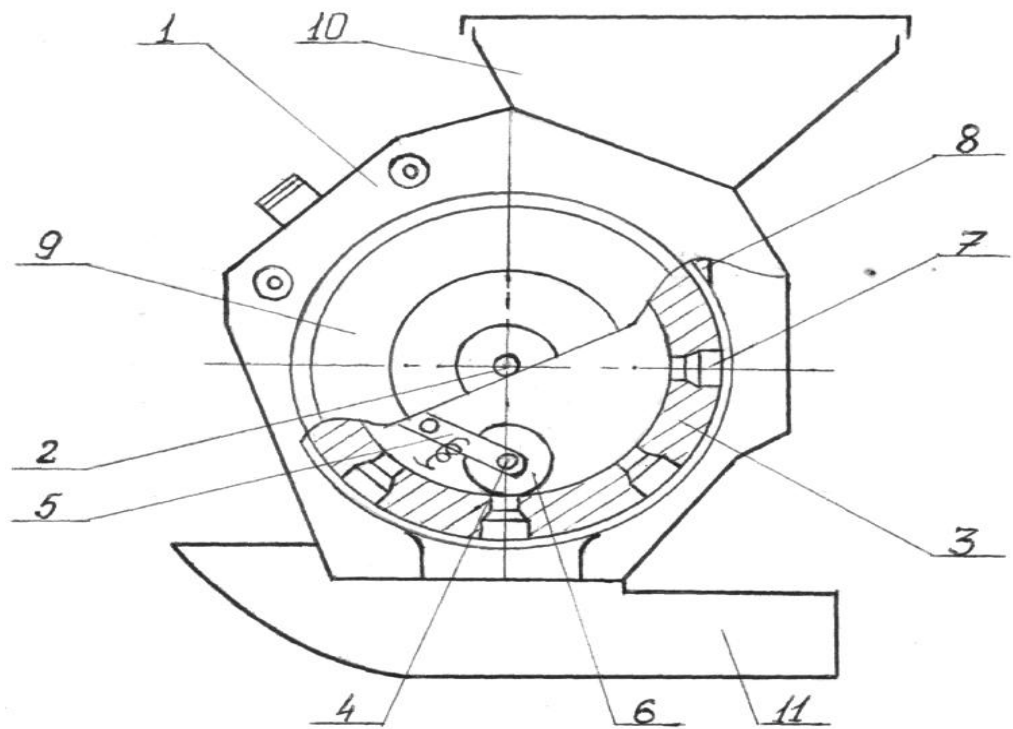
Схема запропонованого висівного апарату: 1 – корпус; 2 – вал; 3 – висівний диск; 4 – вісь; 5 – вилка; 6 – ролик; 7 – комірочка; 8 – камера забору; 9 – кришка; 10 – бункер; 11 – сошник
